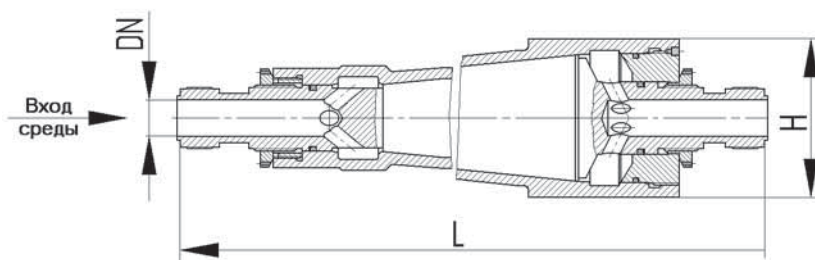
Клапан дроссельный проходной штуцерный
